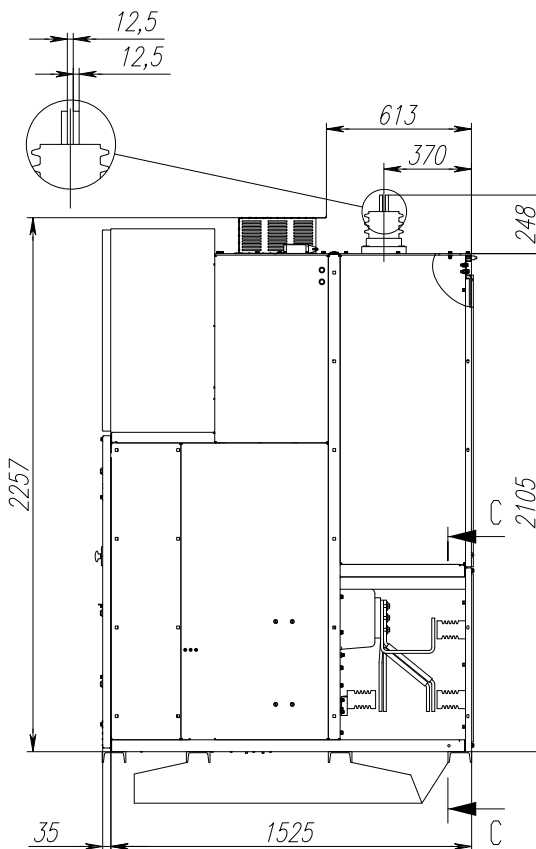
Общий вид и габаритные размеры шкафа К-128 шинного ввода на номинальные токи 2000-4000 А
